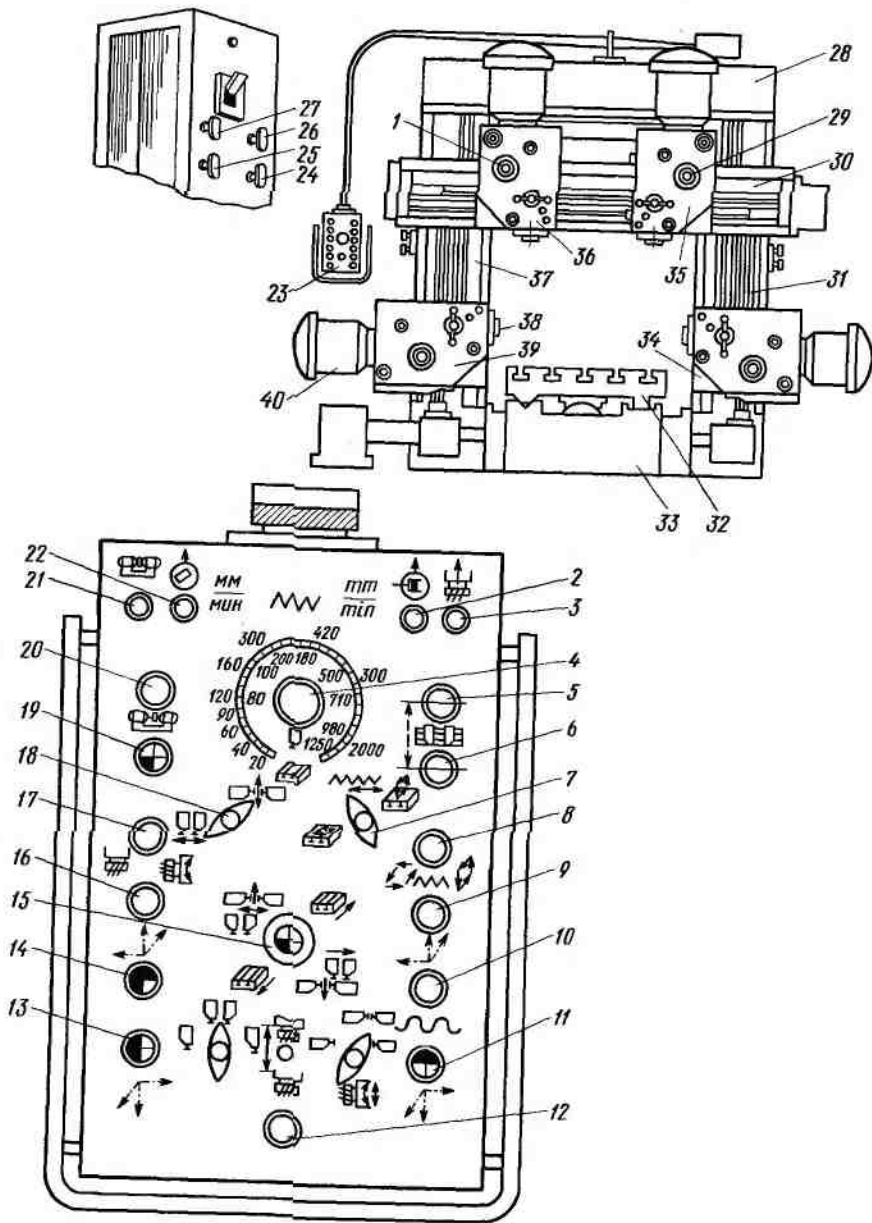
Продольно-фрезерный станок мод. 6610
